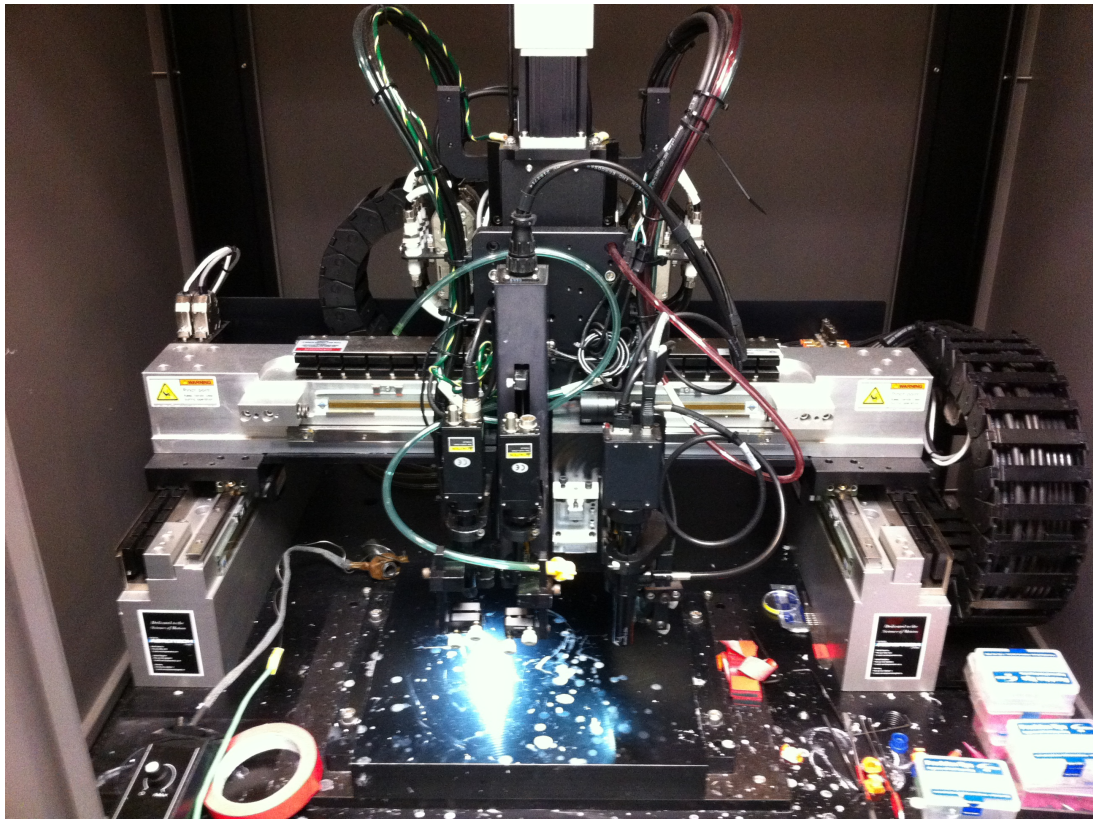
La máquina de rapid prototyping Engineering 3Dn-300.
